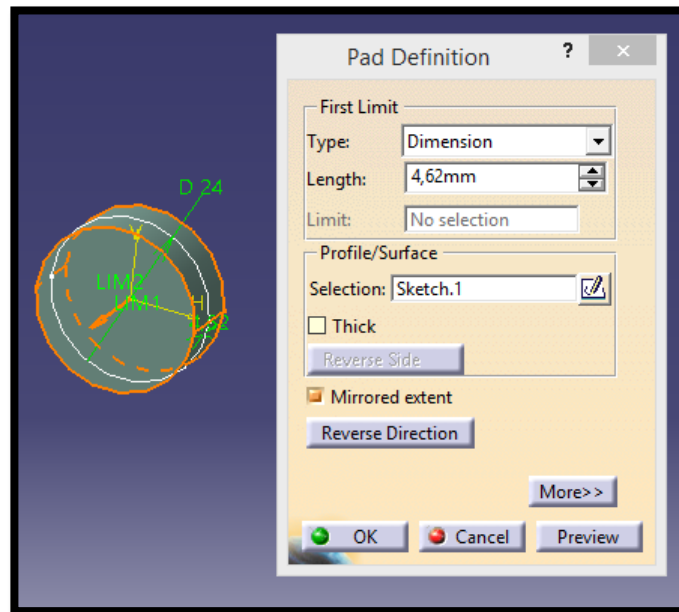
Seat mounting frame 11: Pad brazo oscilante superior
